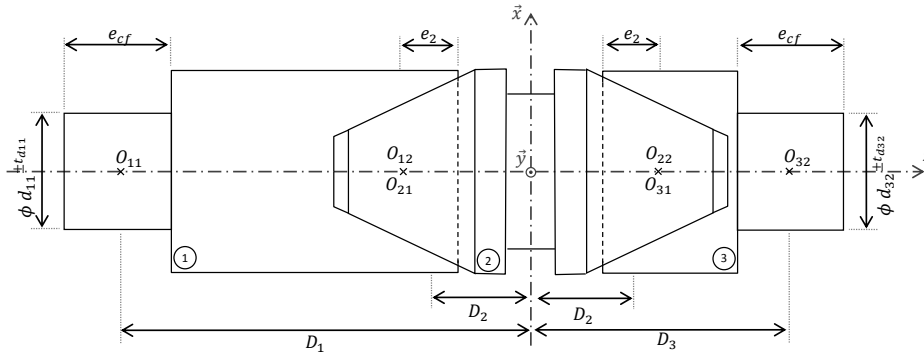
Exemple d'assemblage axisymétrique en série sans jeu
